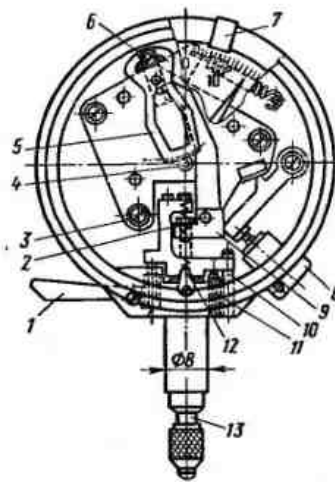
Рычажно-зубчатая измерительная головка типа ИИГ
